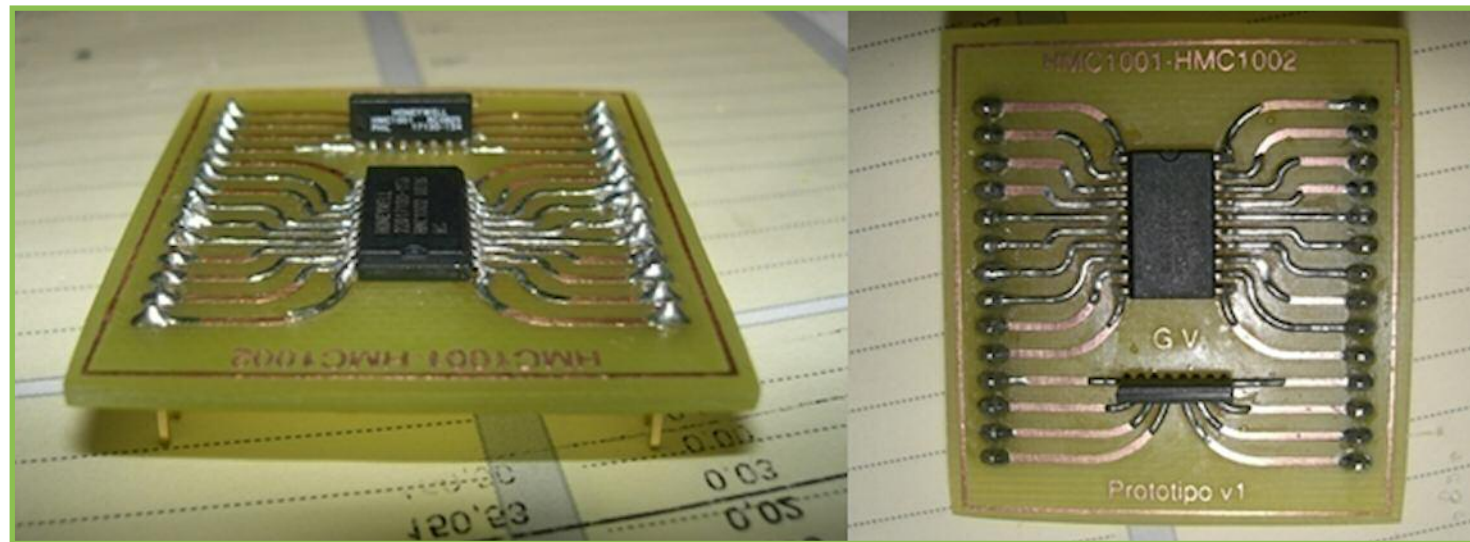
PCB dei sensori terminata dopo la saldatura componenti
